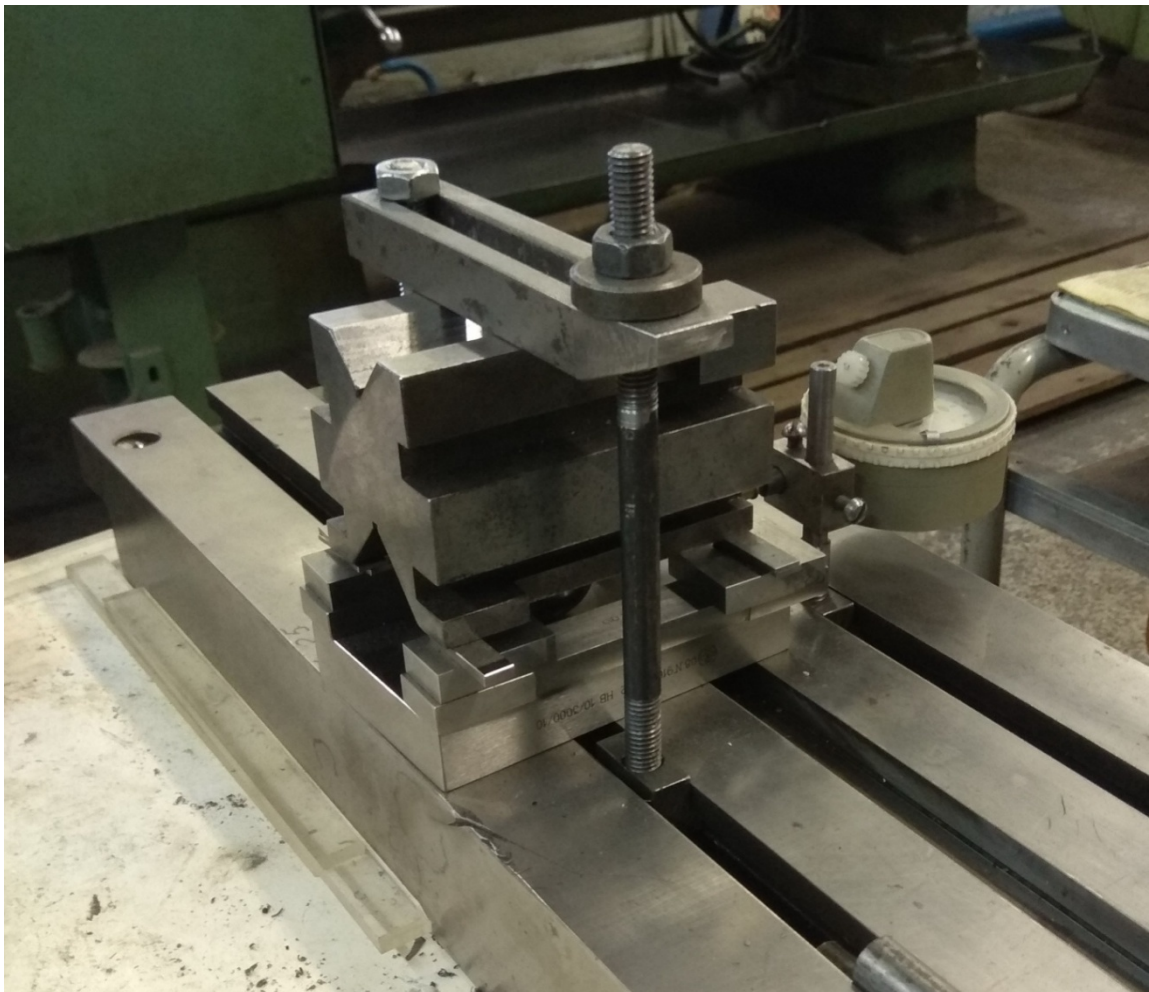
Установка для вимірювання реальної геометрії куль
